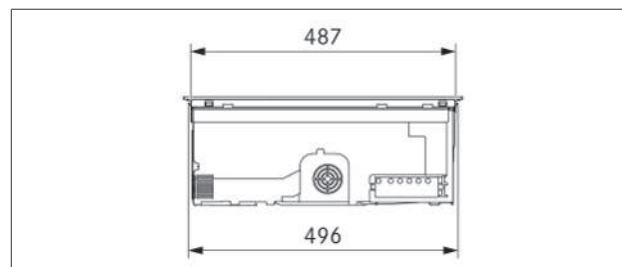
Dimensions de l'appareil - Vue latérale
